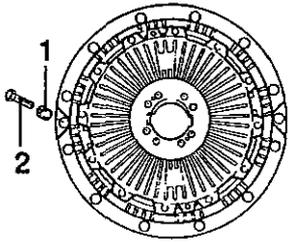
Zwölfpunktbefestigung (Reibklotzausführung)
